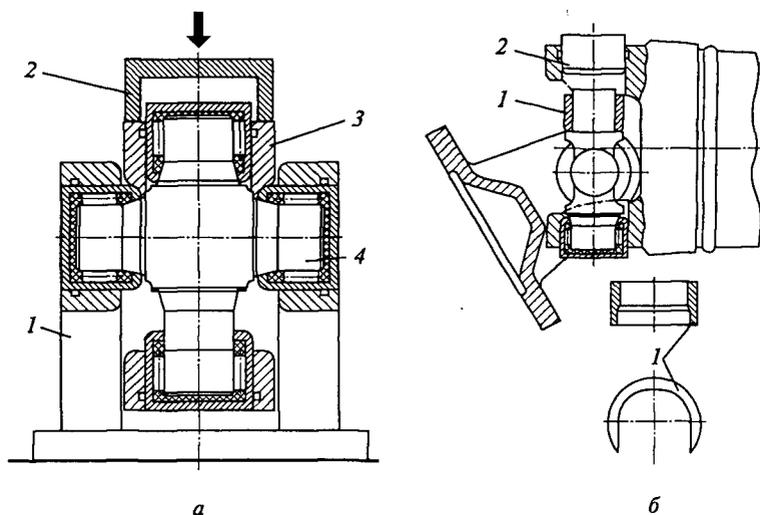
Разборка карданного шарнира (новой конструкции):
